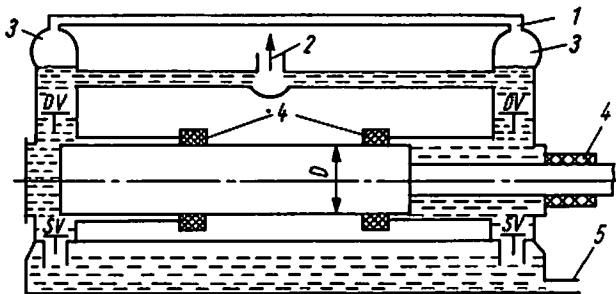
Doppeltwirkende Kolbenpumpe mit Tauchkolben /1/
